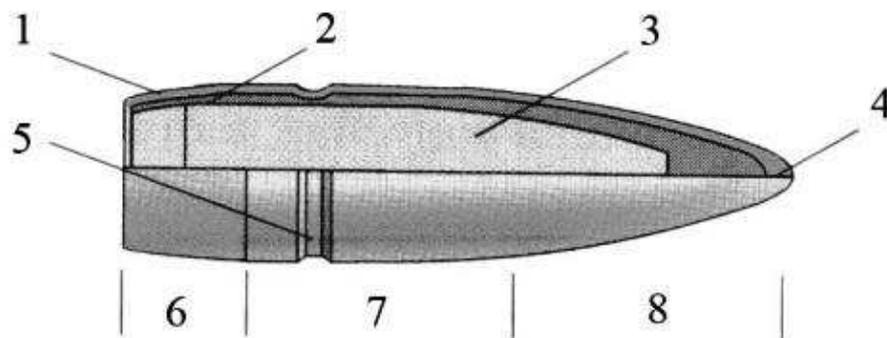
Общее устройство оболочечной пули: 1 – оболочка; 2 – рубашка, 3 – сердечник; 4 – вершинка пули; 5 – канавка; 6 – хвостовая часть; 7 – ведущая часть; 8 – головная часть
